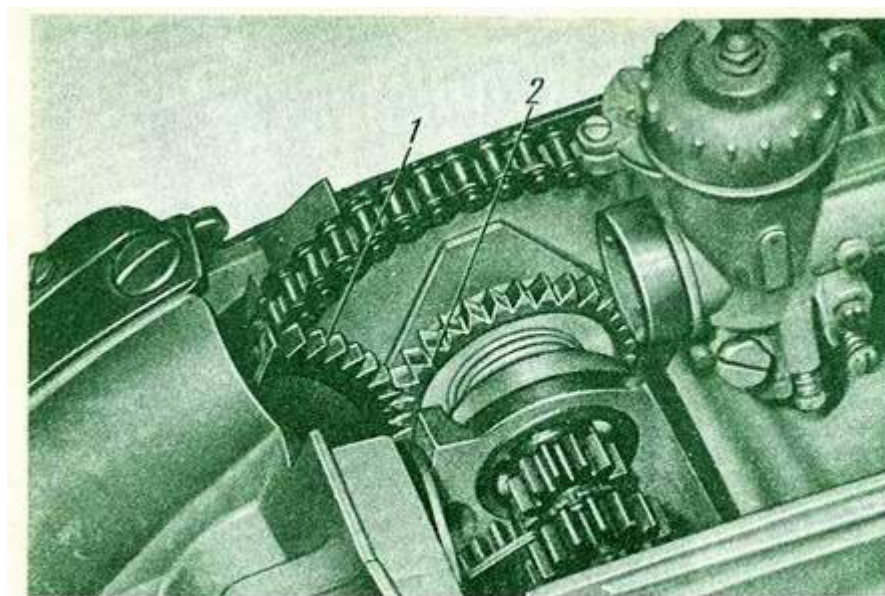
Зубчатый сектор в зацеплении с храповым колесом:
